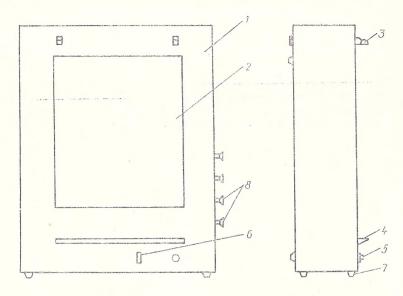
Негатоскоп общего назначения с диафрагмирующими шторками НІЦ-48. Общий вид
